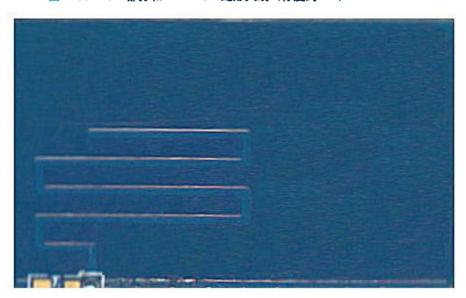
部分和 BLE PCB 蛇形天线(标度约 4:1)
